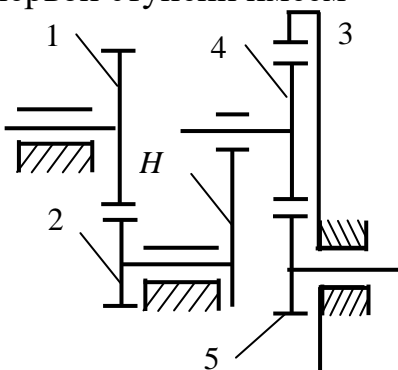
Схема двухступенчатого редуктора с планетарной передачей
